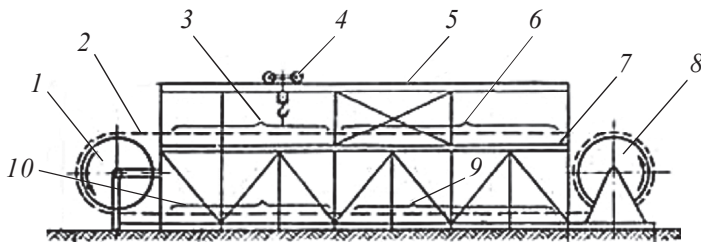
Установка для изготовления полотнищ рулонных заготовок:
